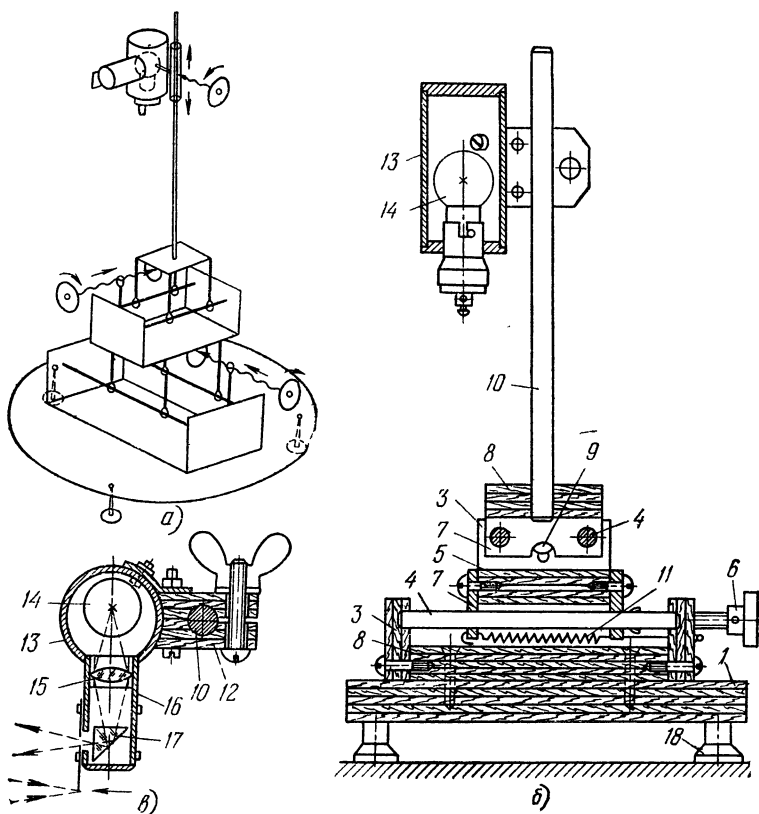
Теневой прибор с суппортом: а — кинематическая схема; б — общий вид, в — конструкция осветителя с конденсором.
